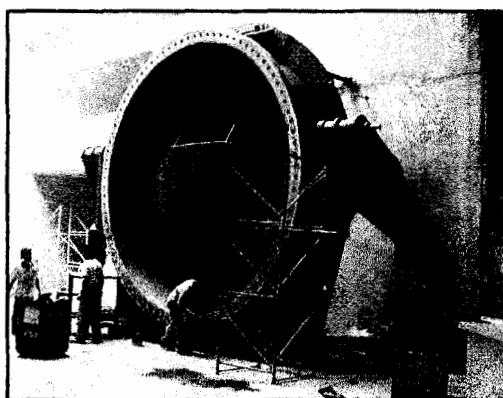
Válvula Mariposa Antes de ser Instalada
